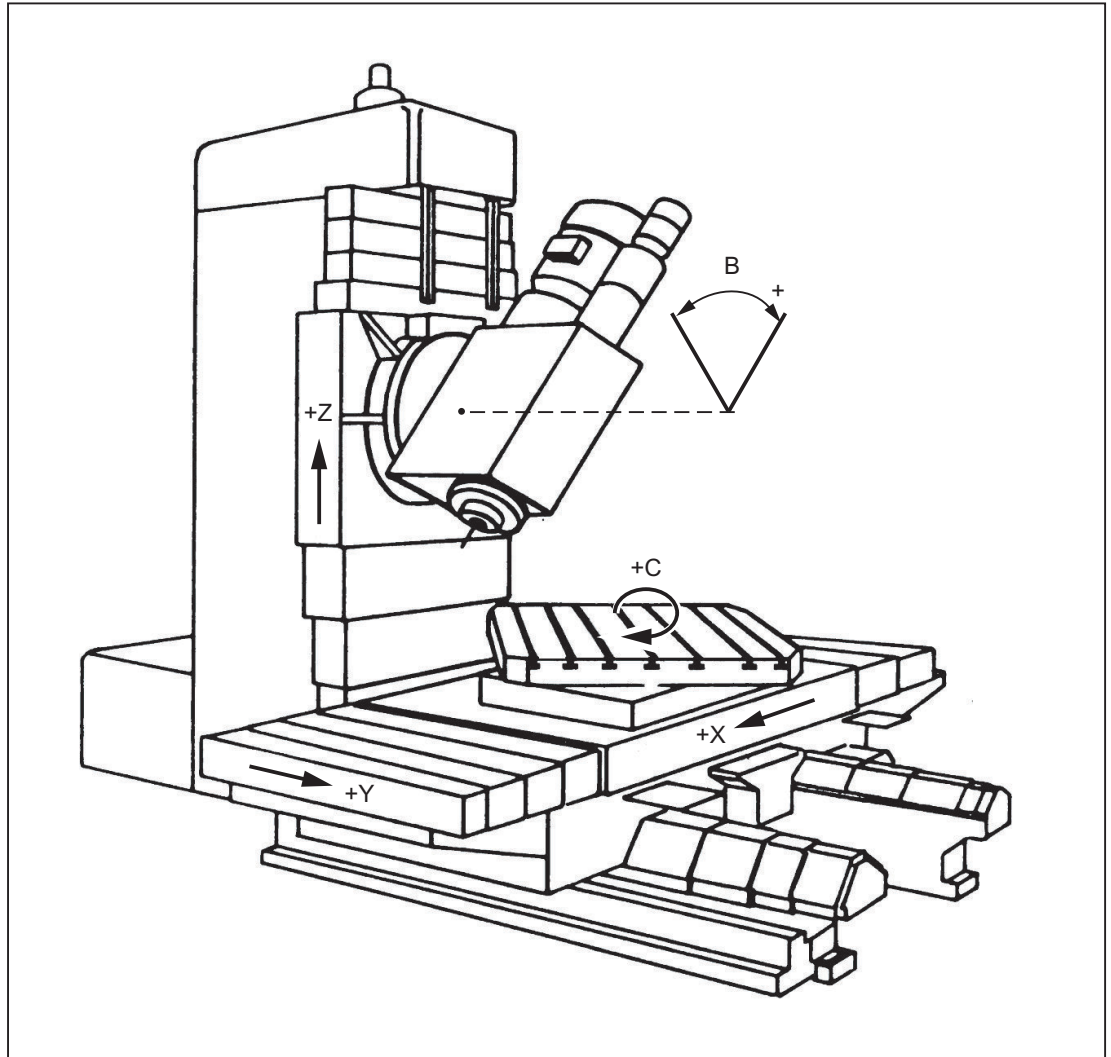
Maschinenachsen X, Y, Z, B, S einer kartesischen Maschine
